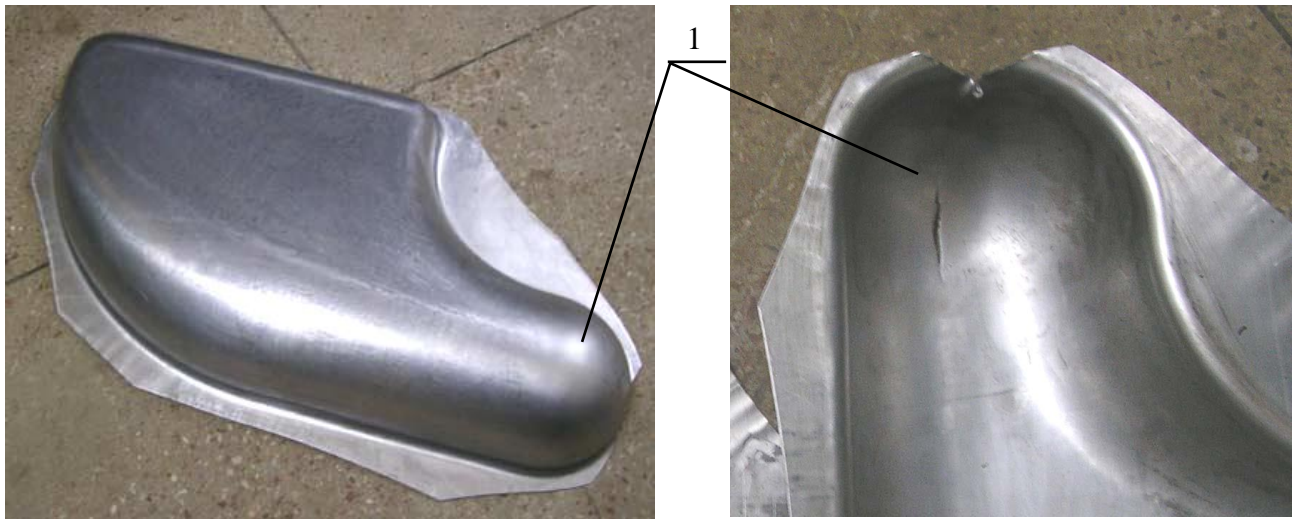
Общий вид штампованного полуфабриката детали «полупатрубок» из алюминиевого сплава АМгбМ из листа толщиной 2 мм: 1 – технологический участок заготовки, использованный для изготовления образцов
